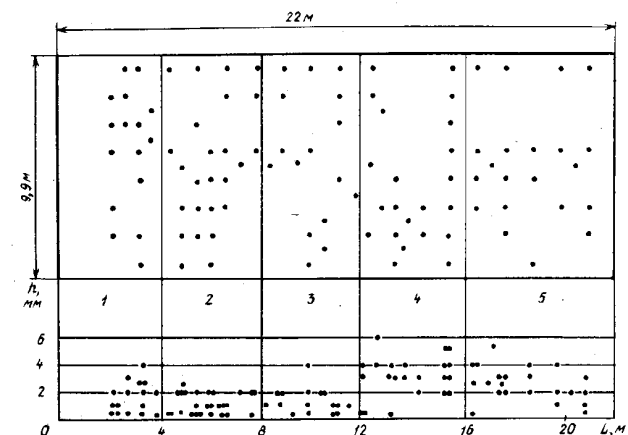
Схема конструкции барабанной сушилки БН 3,2-22
